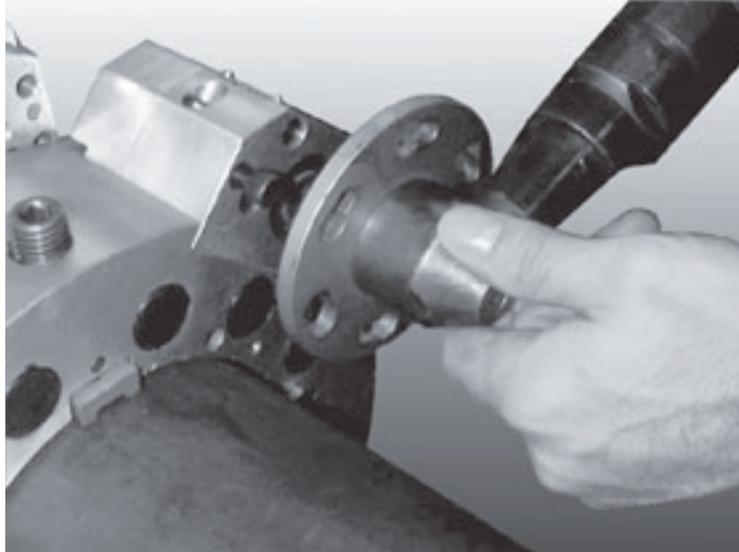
Allineare i fori nella flangia del motore con le due viti nella sede pignone.
